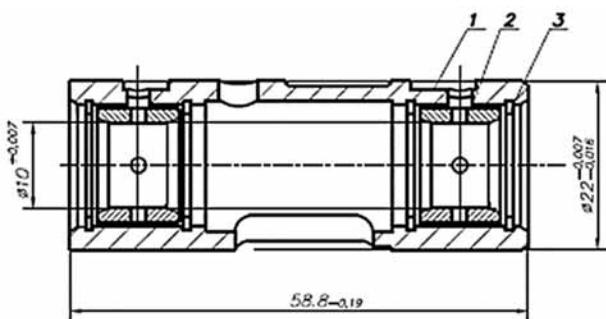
Модульный подшипник турбокомпрессоров ТРК 7С-6:
